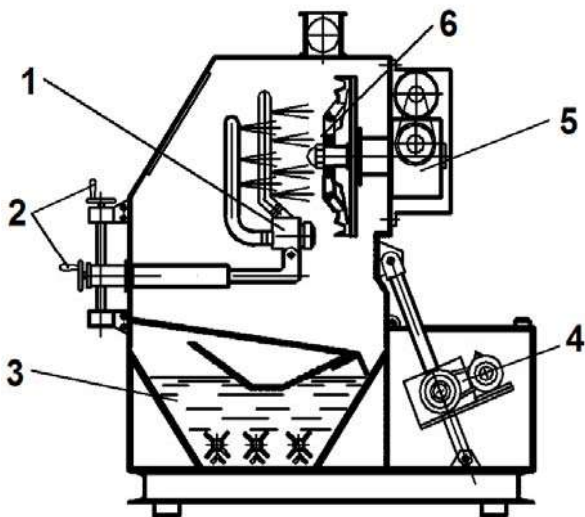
Установка для струминно-абразивної обробки деталей з виштовхувальними баками, що діють по черзі
